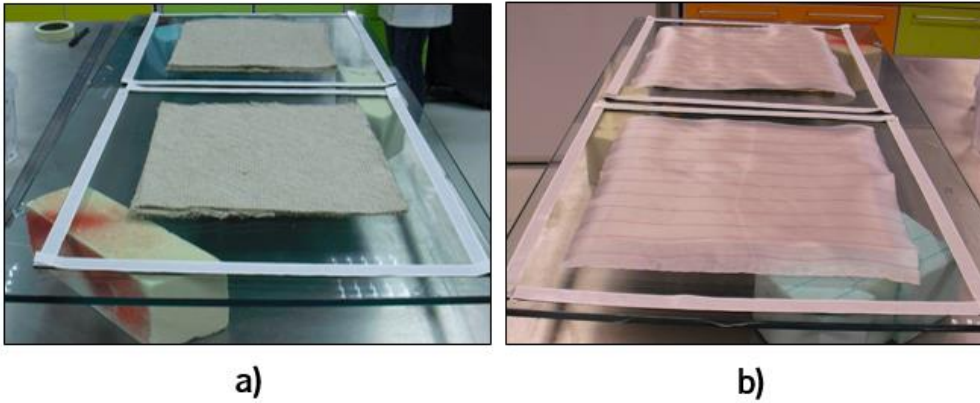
Posicionamento das fibras de reforço com dimensões (300mm x 300mm) (a) e, sob estas o “peel ply” com dimensões (350mm x 350mm) (b)
